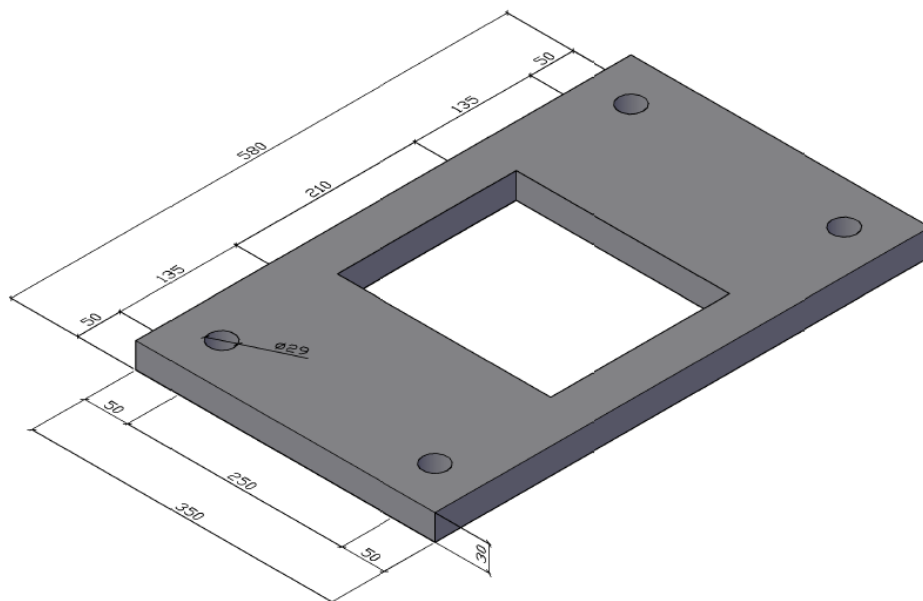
Placa de aplicação de ações (dimensões em mm)
